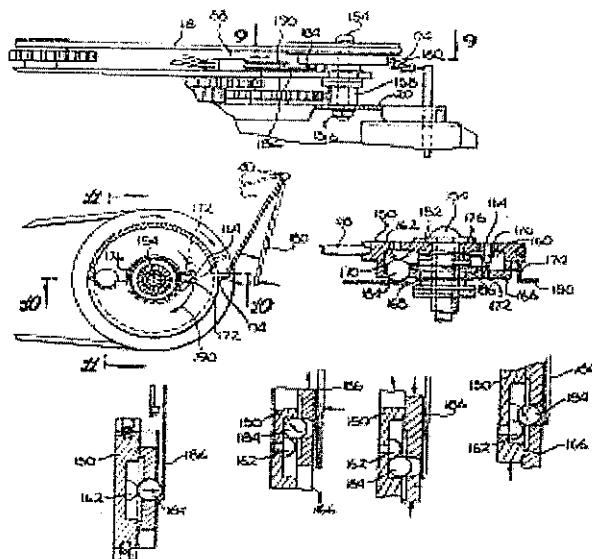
ลักษณะการทำงานของเครื่อง Plastic Sheet Cleaning Machine
